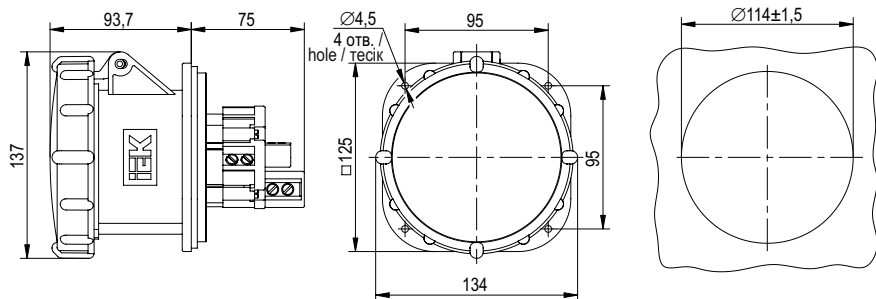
Габаритные размеры соединителя типа ССИ-445 / Figure 13 – Overall dimensions of plug and socket-outlets SSI-445 / Сурет 13 – ССИ-445 типті жалғастырғыштардың габариттік өлшемдері
